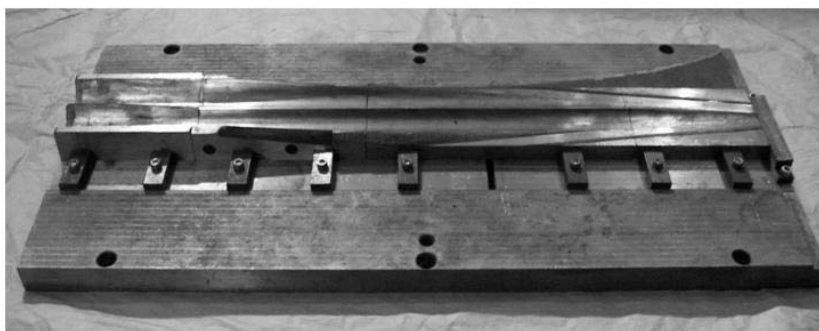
Инструмент для поперечно-клиновой прокатки шаров
